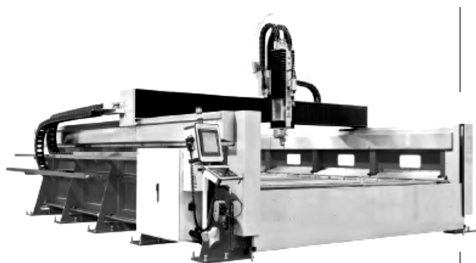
Конструкция установки гидроабразивной резки для обработки объемных деталей
